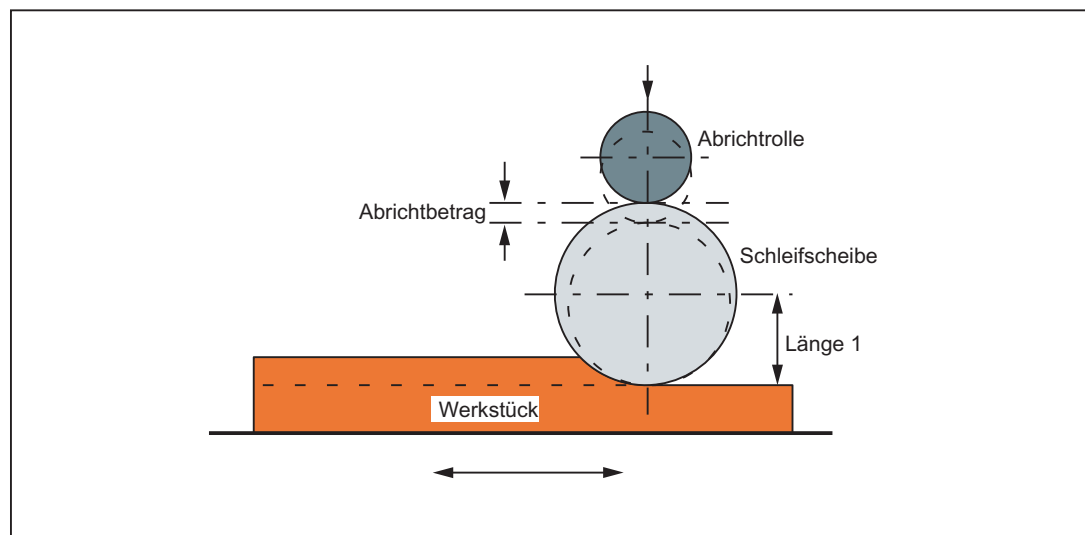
Abrichten während der Bearbeitung mit einer Abrichtrolle
